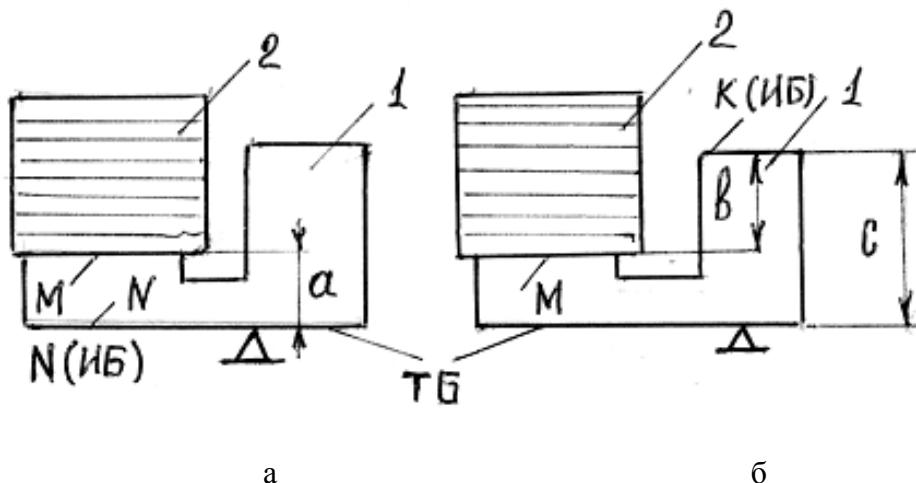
Фрезерование плоскости: 1 – заготовка, 2 - фреза
